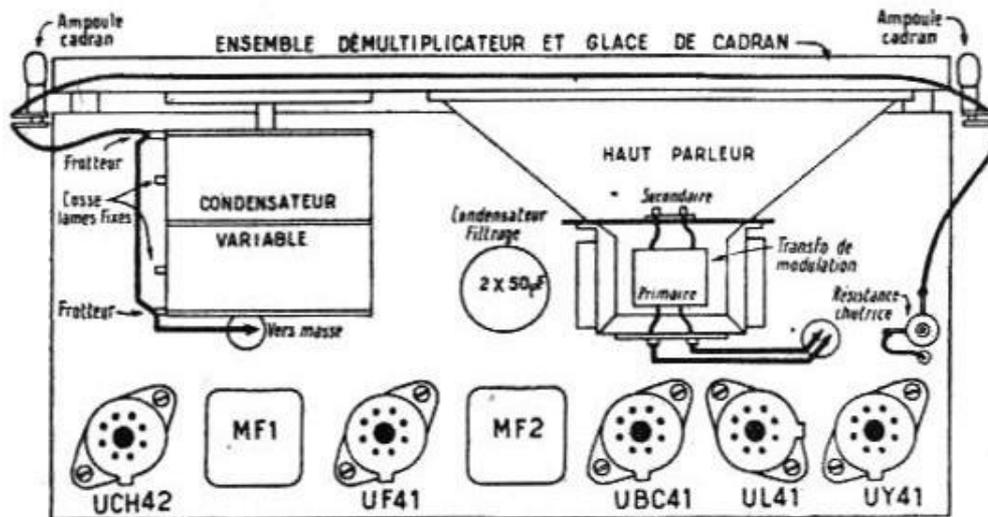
Montage mécanique du « MENUET » châssis vu du dessus
